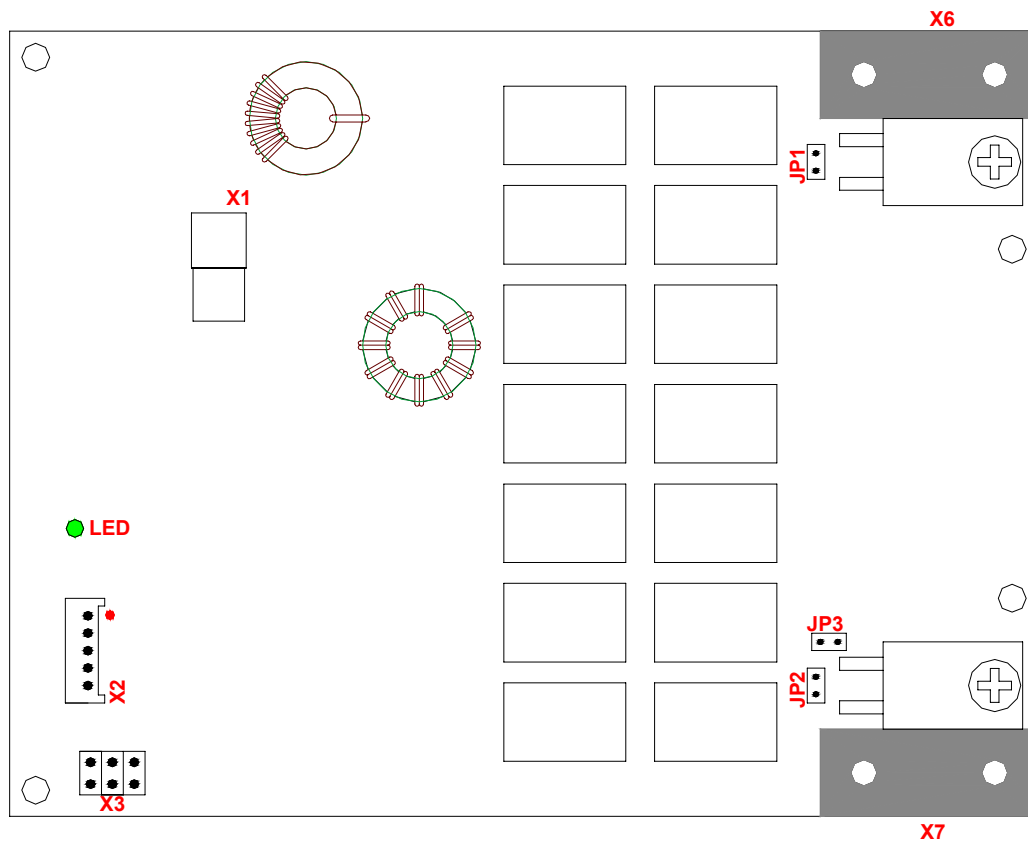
Anschlussbuchsen und –klemmen, Einstellelemente und LED
